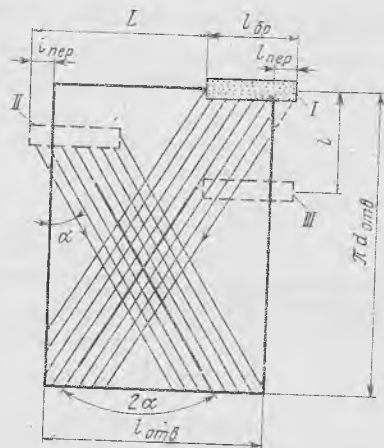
Развертка сетки следов обработки при хонинговании цилиндра блока:
